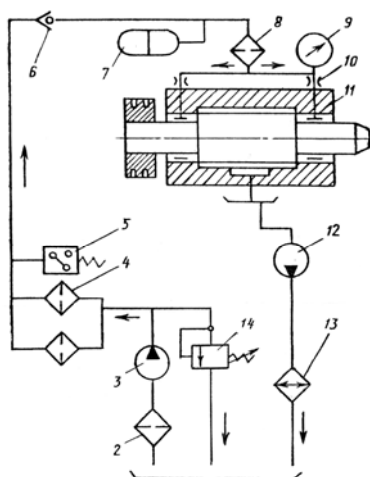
Схема смазочной системы гидростатических опор шпинделя металлорежущего станка:
